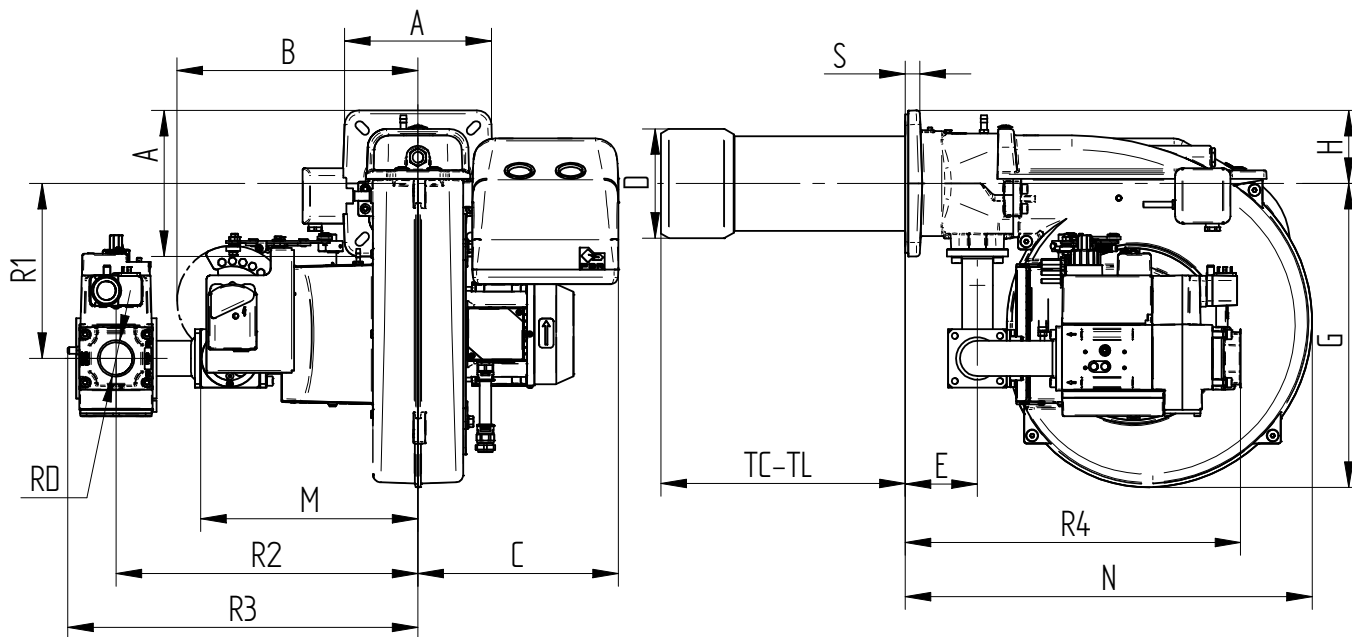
РАЗМЕРЫ GAS XP60/MCE-EVO
